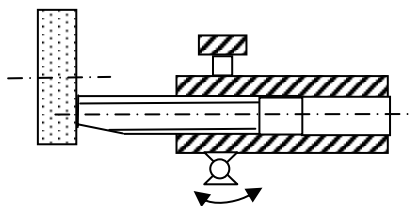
Заточка торцевых режущих кромок в приспособлении
